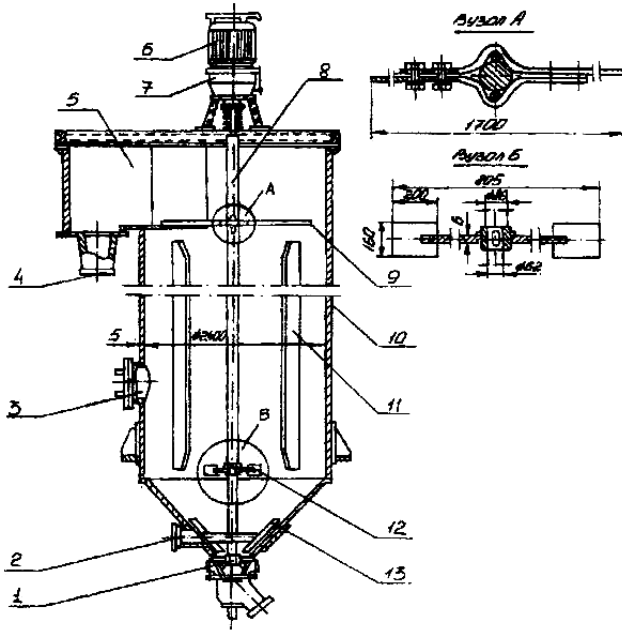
Передефекатор ПР-3: 1 – підшипник; 2 – вхідний штуцер; 3 – люк; 4 – патрубок для виведення соку; 5 – порожина для піни; 6 – електродвигун; 7 – редуктор; 8 – вертикальний вал; 9, 12, 13 – мішалки; 10 – вертикальний циліндр; 11 – контропаті
